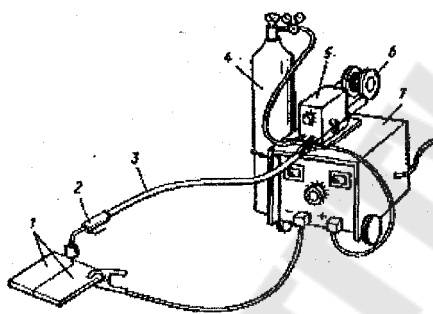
Пост для полуавтоматической сварки в среде CO_2 :
